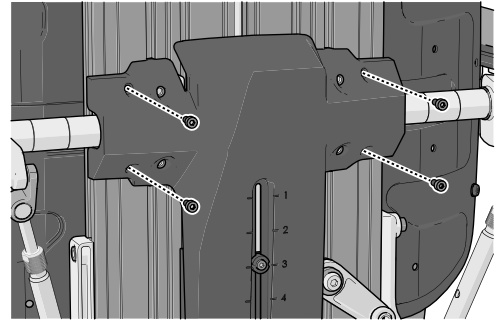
Die Anbringensorte der vier Schrauben, die die Kunststoffabdeckung sichern.
